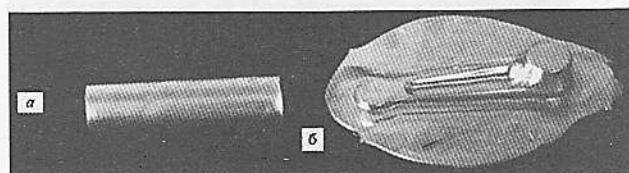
а — мерная заготовка; б — штампованная поковка «Качалка», изготовленная за две штамповки с промежуточными операциями обрезки облоя, травления, зачистки, нагрева. Сплав АК8.
